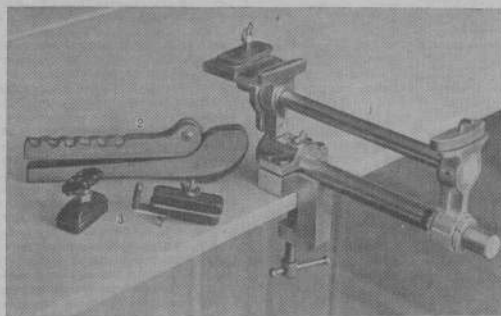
Инструменты и приспособления для натяжки ракеток: 1 — ступовое устройство, 2 — натяжное устройство лямбобричного типа, 3 — стопорные накладки
